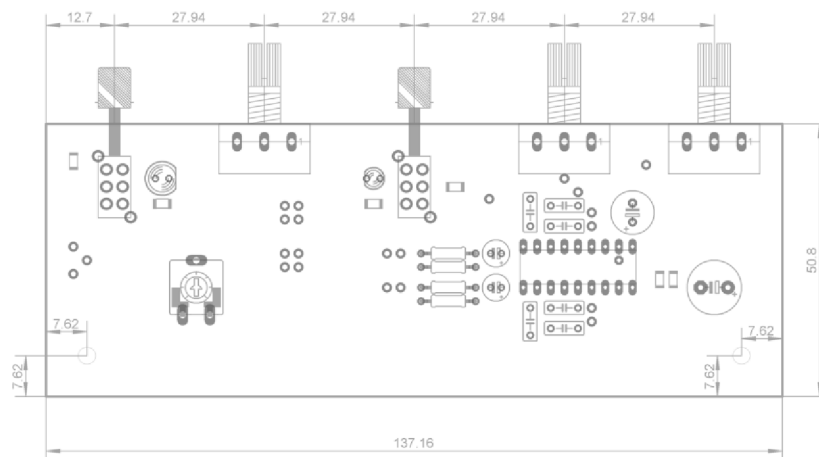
Rozměry DPS pro stereo předzesilovače.
